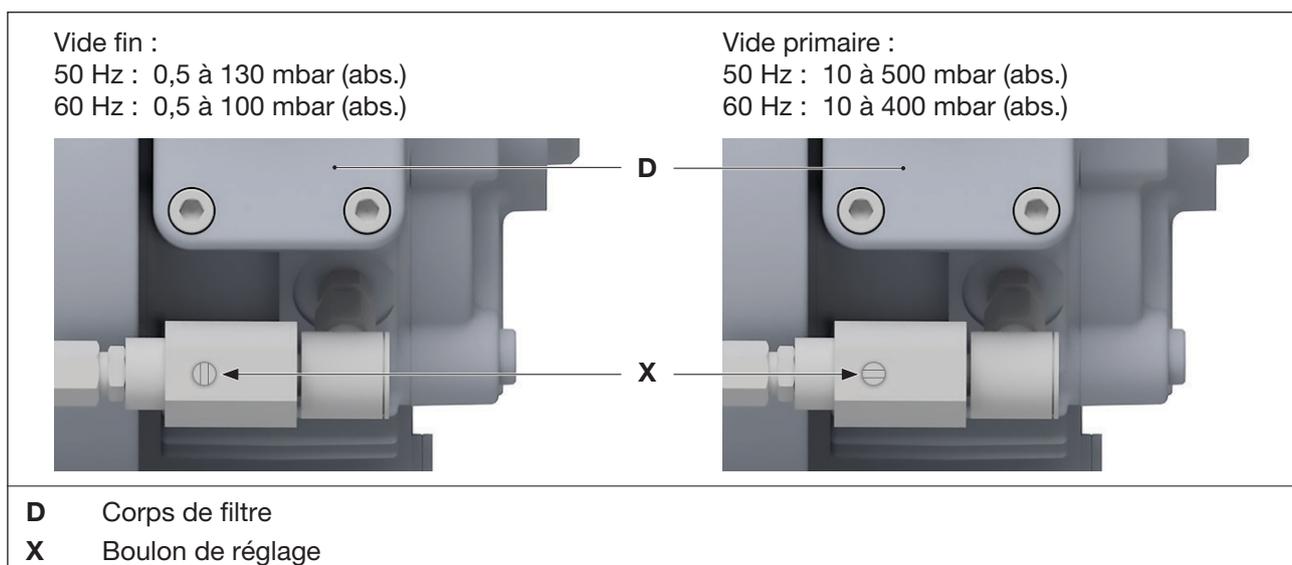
Réglez la plage de travail sur la variante VCE 25 (09)
